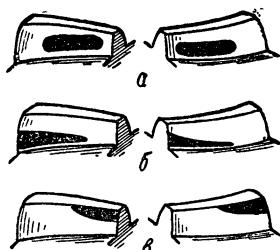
Отпечатки краски на зубьях ведомой шестерни главной передачи
